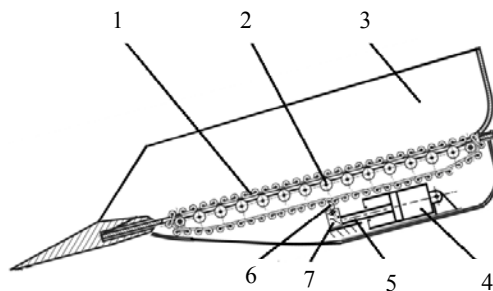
Ковшовый рабочий орган с конвейерным днищем в виде замкнутой ленты, связанной с приводными гидроцилиндрами через стопорные фиксаторы: 1 — замкнутая лента; 2 — ролики; 3 — боковые стенки; 4 — гидроцилиндр; 5 — шток гидроцилиндра; 6 — фиксатор; 7 — пружина
